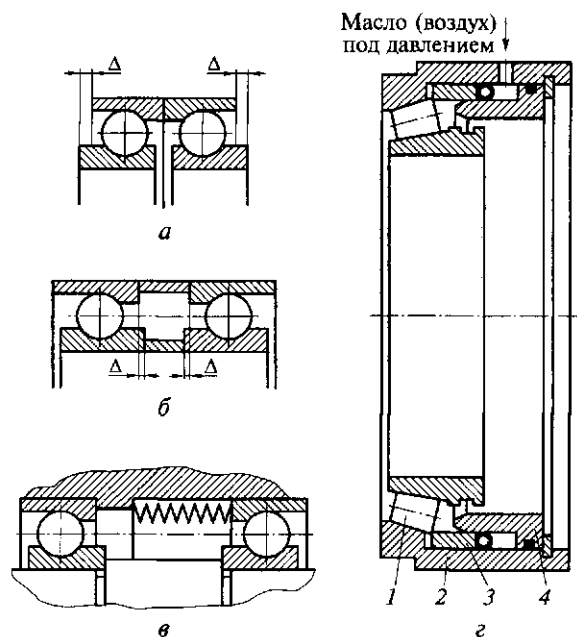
Способы создания натяга в подшипниках качения:
